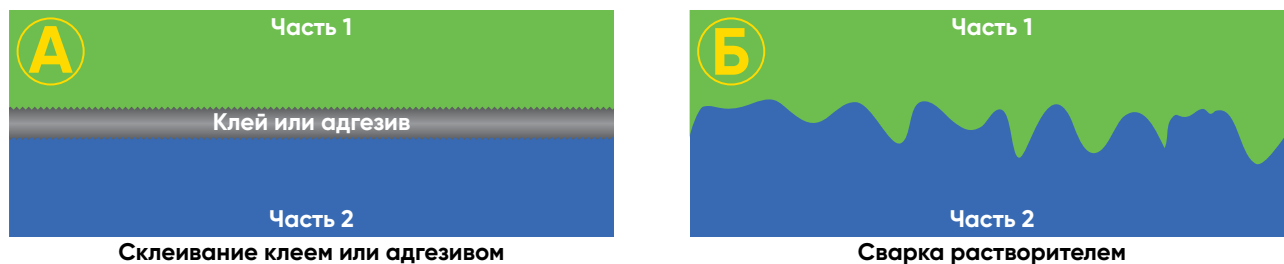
Клеевое соединение и сварка растворителем («холодная сварка»)
